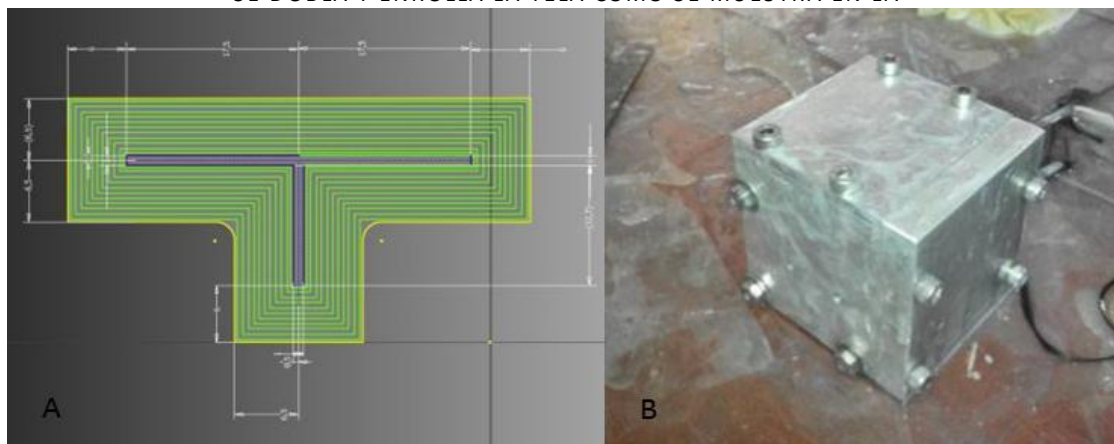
A) DIAGRAMA DE ENROLLADO B) MOLDE CERRADO.
